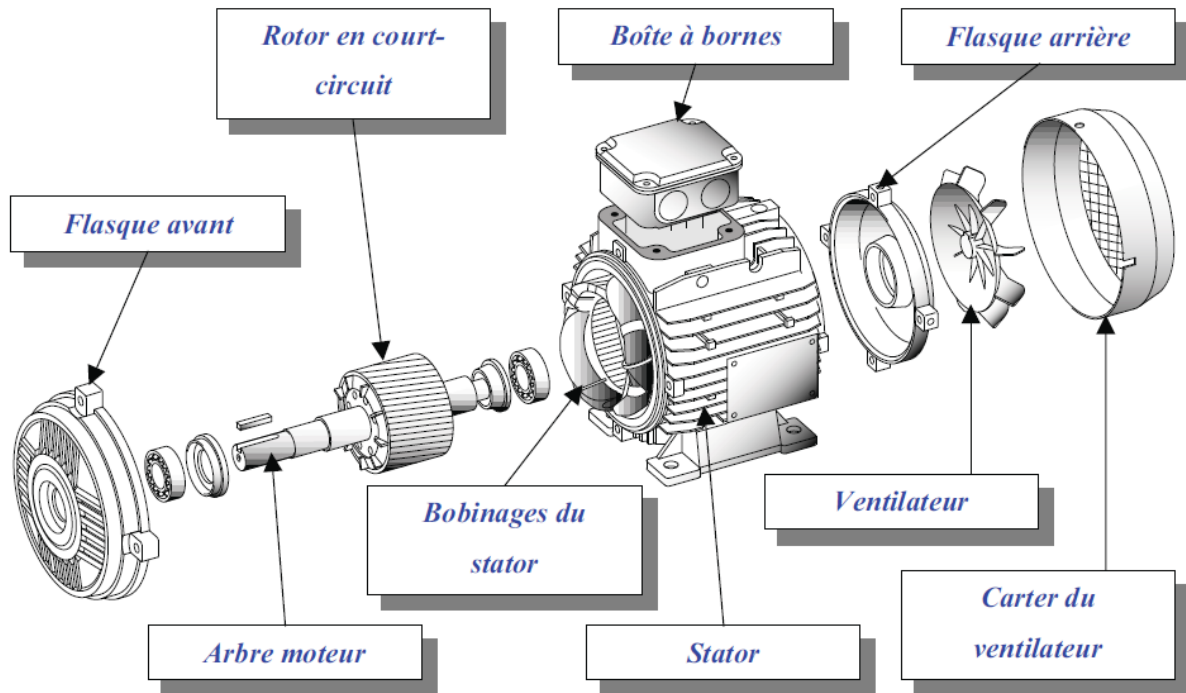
vue éclatée d'un machine asynchrone triphasé à rotor en cage d'écureuil
